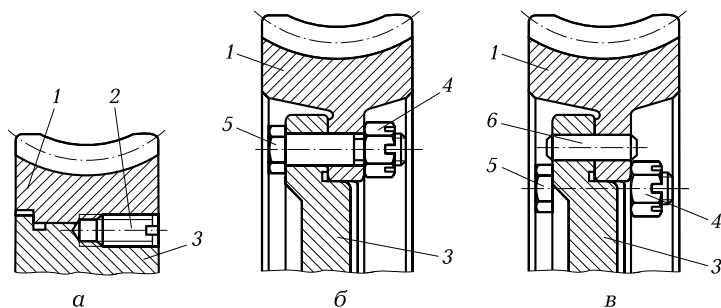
Схема сборки червячного колеса при помощи винта (а), болта (б), болта и штифта (в):
